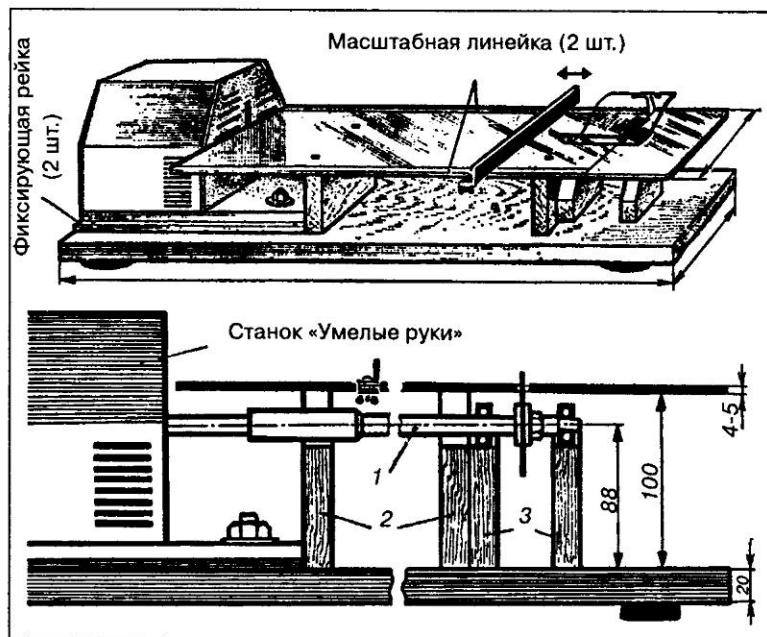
Деревообрабатывающий станок на базе станка «Умелые руки»:
